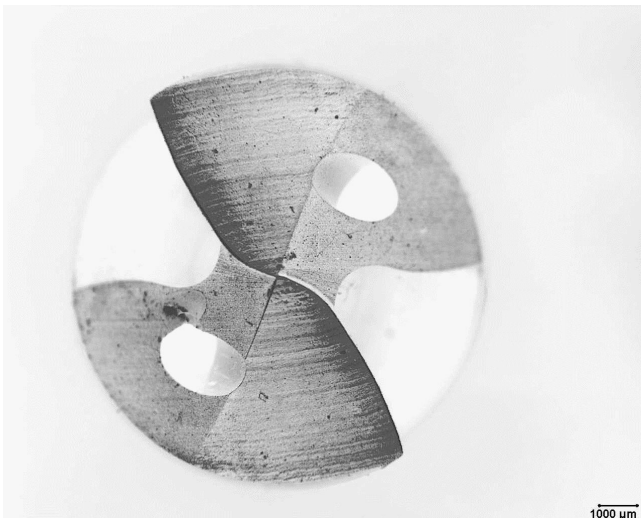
Eingesetzte Spiralbohrer für die Trockenbearbeitung in der Stirnansicht
